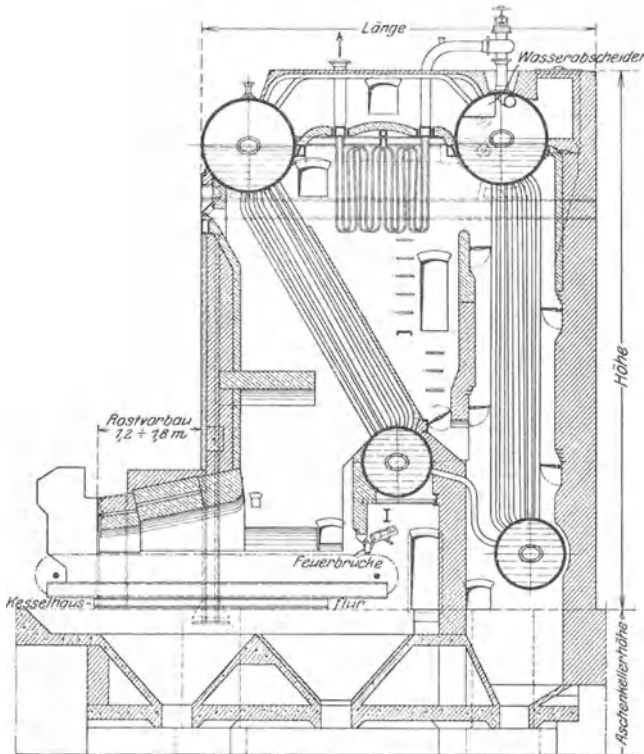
Steilrohrkessel, Bauart Steinmüller, mit Wanderplanrost, Pendelstauer und eingebautem Überhitzer.
